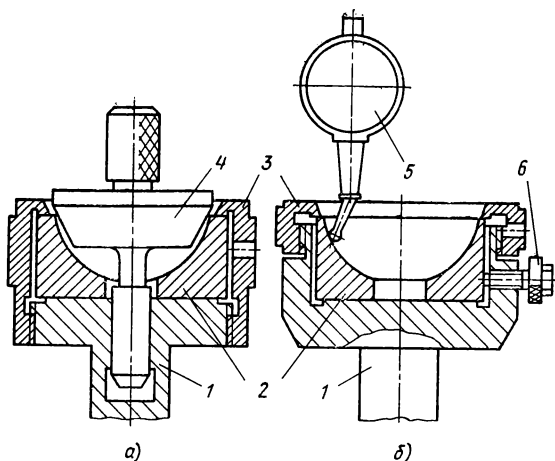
Установка деталей на доводочном станке по калибру (а) и индикатору (б):
